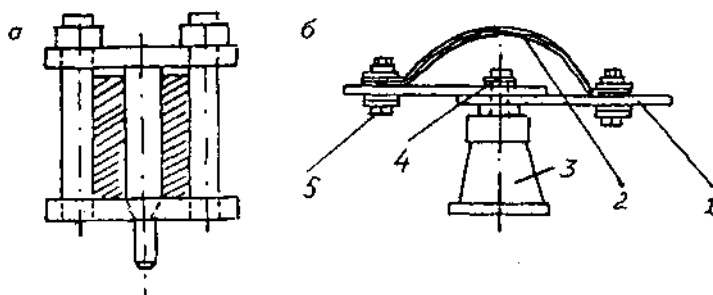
Шинодержатель и шинный компенсатор для плоских шин: а — типа ШПРА-1с; б — компенсатор для болтового соединения шин; 1 — шина; 2 — компенсатор; 3 — опорный изолятор; 4 — пружинящая шайба; 5 — болт
